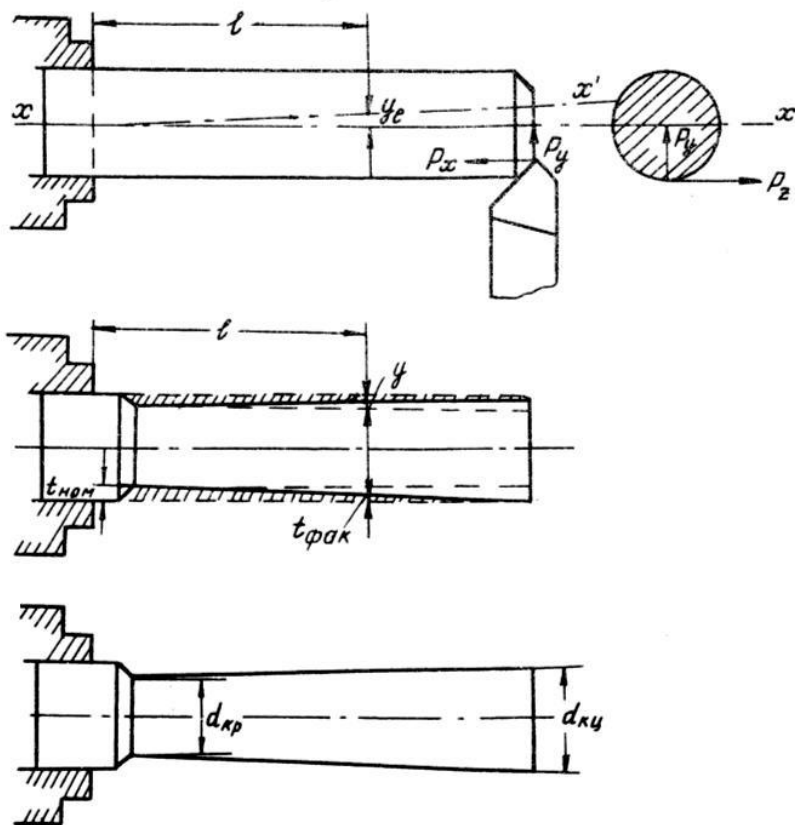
Схема проточки образца, закрепленного консольно в патроне токарного станка
